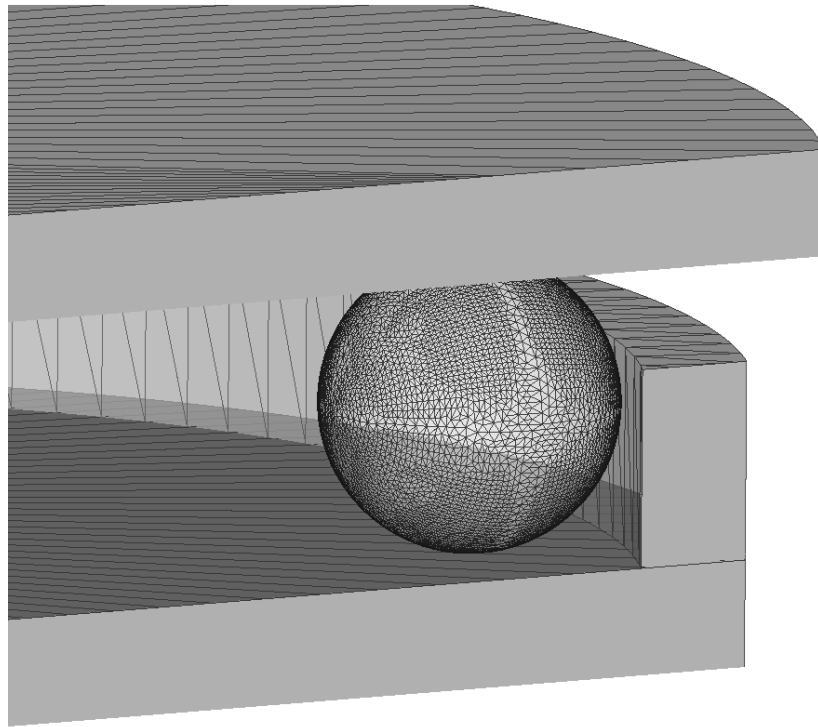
Геометрия инструментов и заготовка с конечно-элементной сеткой
